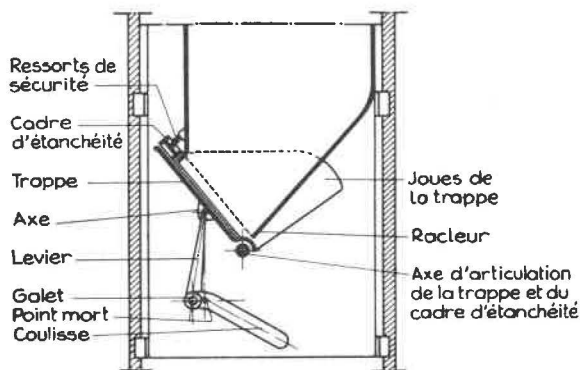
Trappe « PIC-SBM » brevetée — détails.
